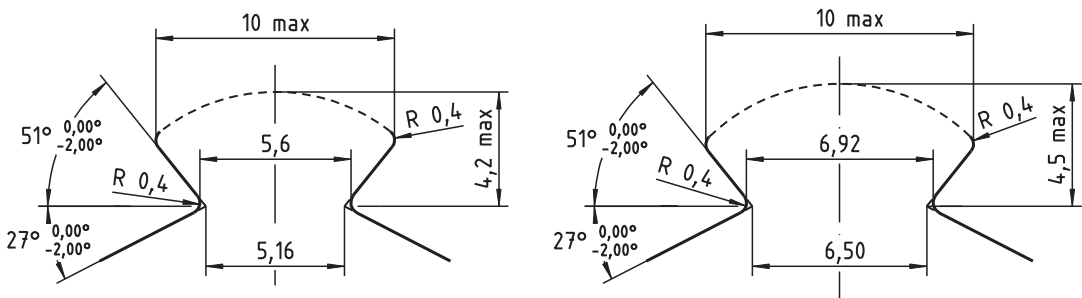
Klemmrillen des Fahrdrabtes nach EN 50149 (Profil A – links, Profil B – rechts)
